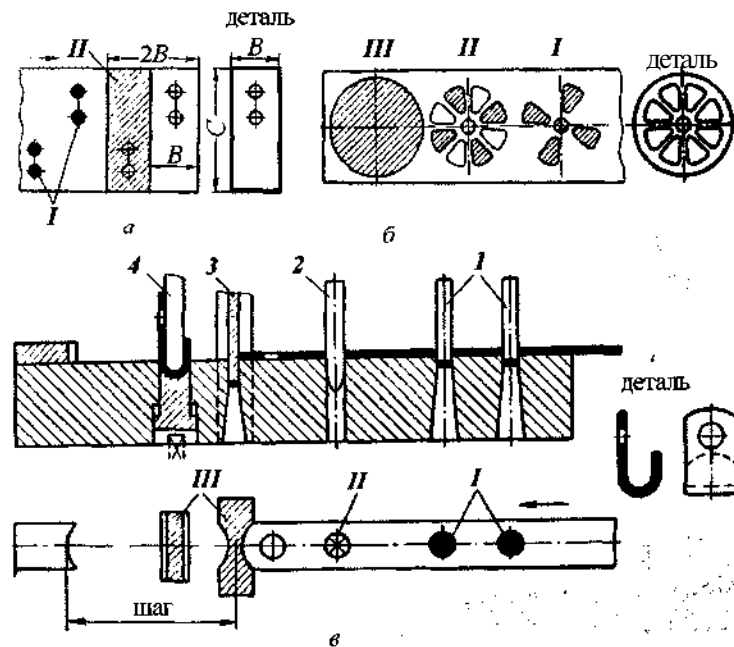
Порядок штамповки в штампах последовательного действия: *a* — при пробивке и отрезке; *б* — при пробивке нескольких отверстий и вырезке; *в* — при пробивке, отрезке и гибке
